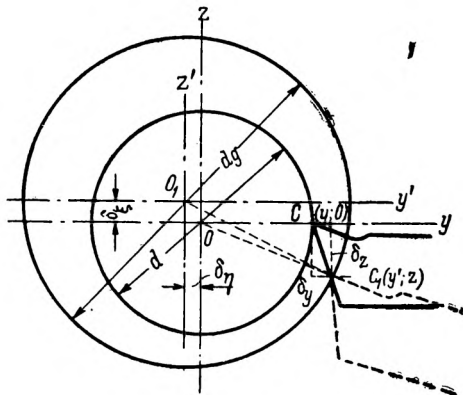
Положение режущей кромки реза при прогибе заготовки.
